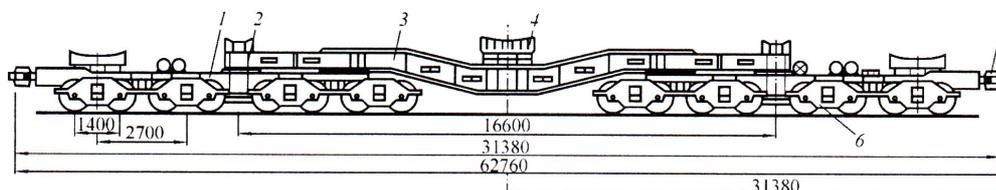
Шестнадцатисный сцеп тридцатисного транспортера сцепного типа
